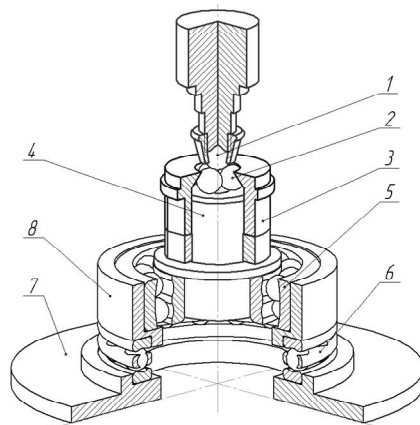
Робочий вузол установки для чотирикулькової схеми
